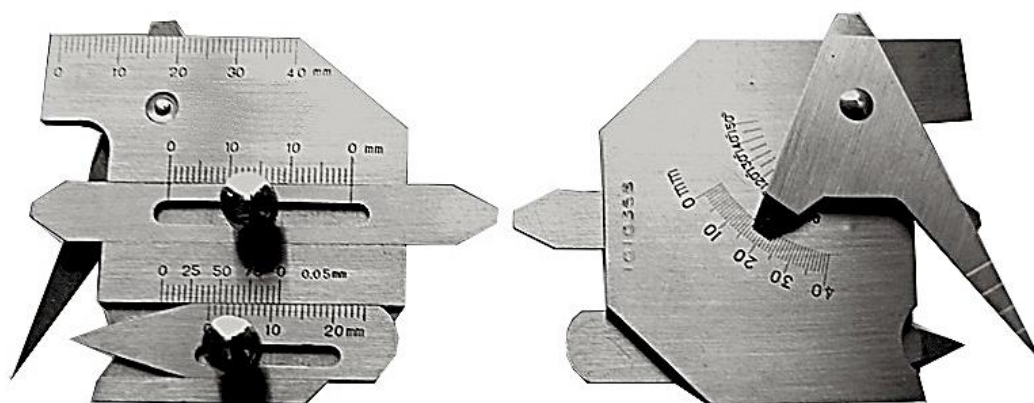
Шаблон зварювальника WG-2 [18]
